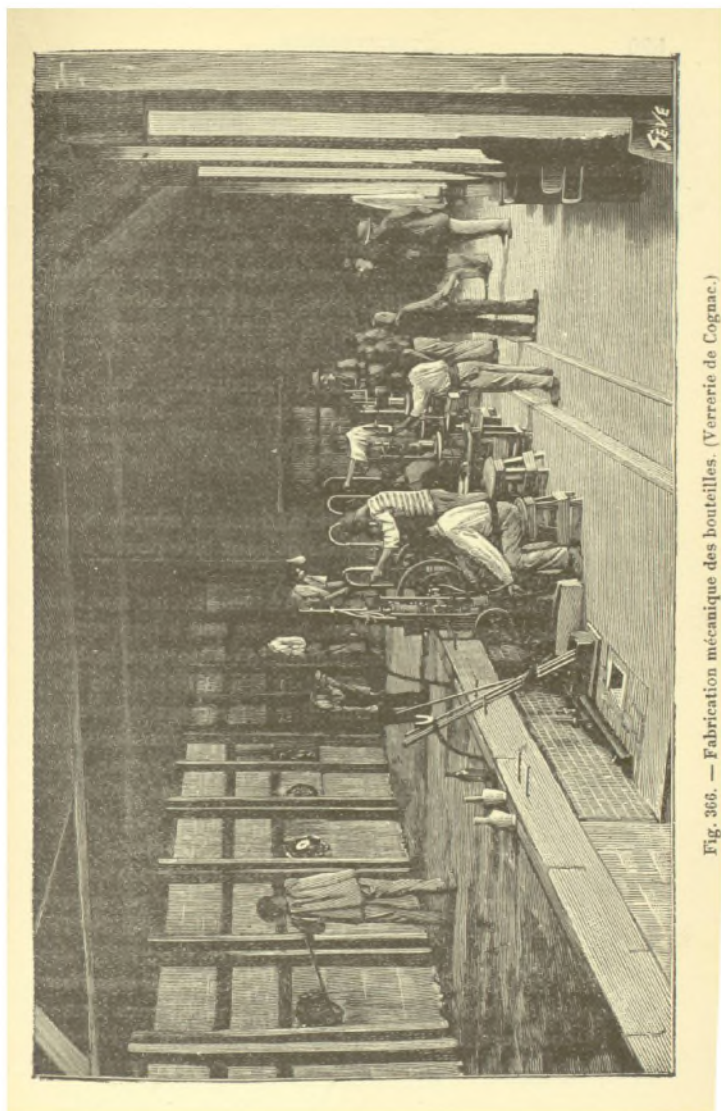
Fabrication mécanique des bouteilles. (Verrerie de Cognac.)
